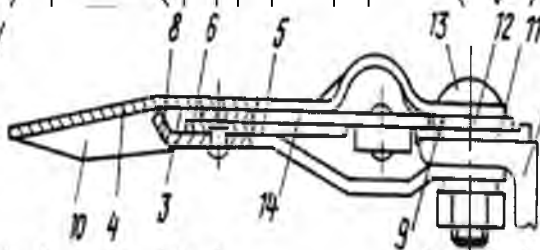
Самогіджамний ріжучий апарат прибиральної машини: 1 - пальцевий брус; 2 - палець; 3 - основа; 4 - верхня секція; 5, 9 - привалочна площа; 6 - протирижуча пластина; 8 - носок; 10 - жолобчата трапецеїдальна формовка; 11 - пластина тертя; 12 - проміжна прокладка; 13 - болт; 14 - сегмент
